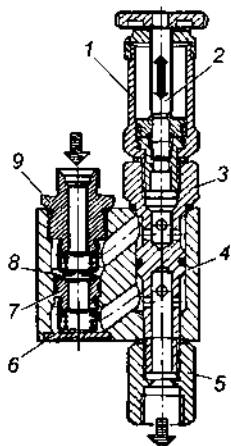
Ручной топливоподкачивающий насос: 1 — цилиндр; 2 — рукоятка насоса с поршнем; 3 и 5 — штуцеры; 4 — корпус; 6 — пружина; 7 — нагнетательный клапан; 8 — пластинчатая пружина; 9 — всасывающий клапан
